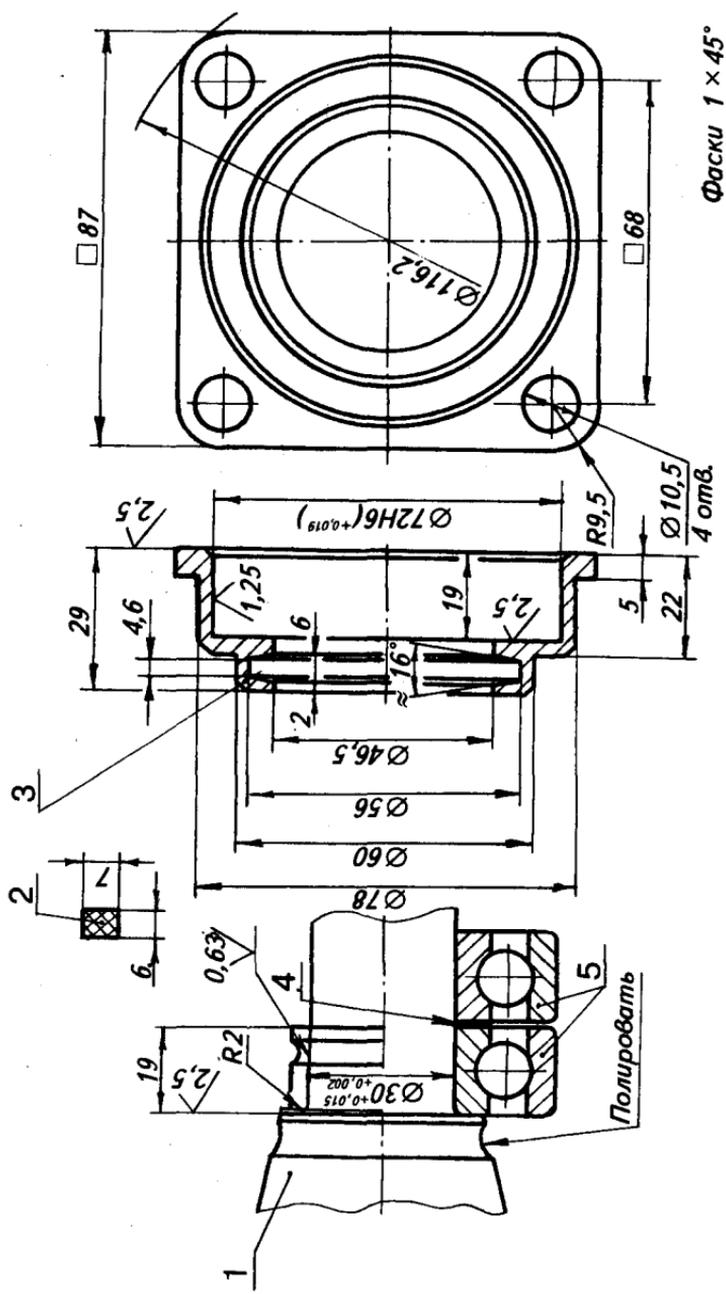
Установка двух подшипников на полуось: 1 — полуось; 2 — профиль сечения войлочного сальника; 3 — крышка; 4 — прокладка ( $d \times D = 30,2 \times 44$  мм); 5 — подшипник (306, 2 шт.).
